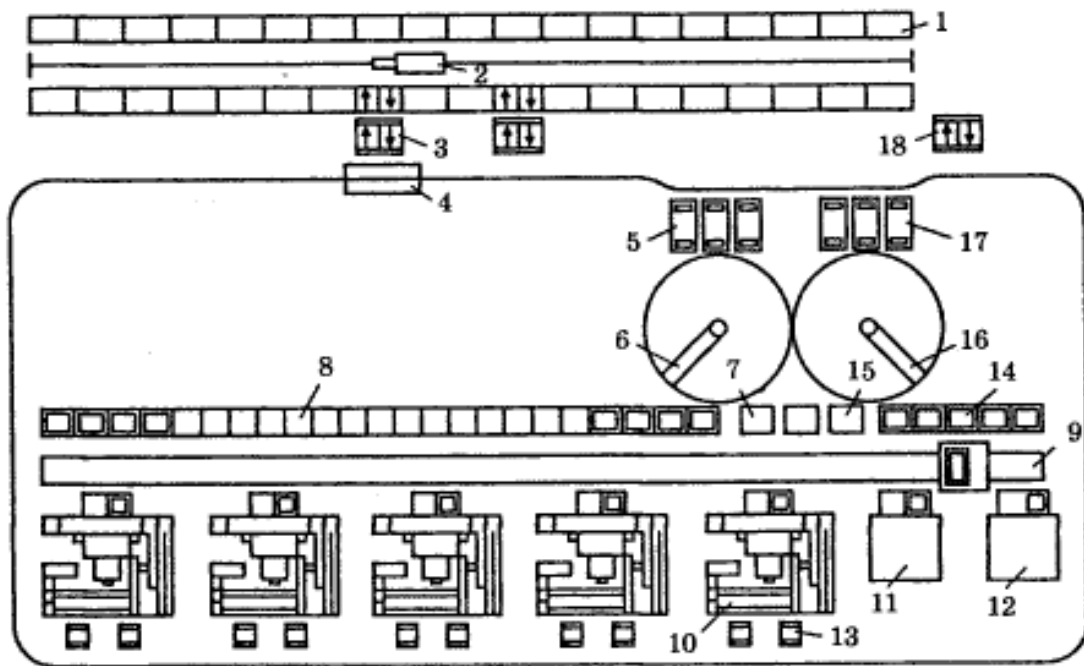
Структура комплексу для обробки корпусних деталей автомобіля
